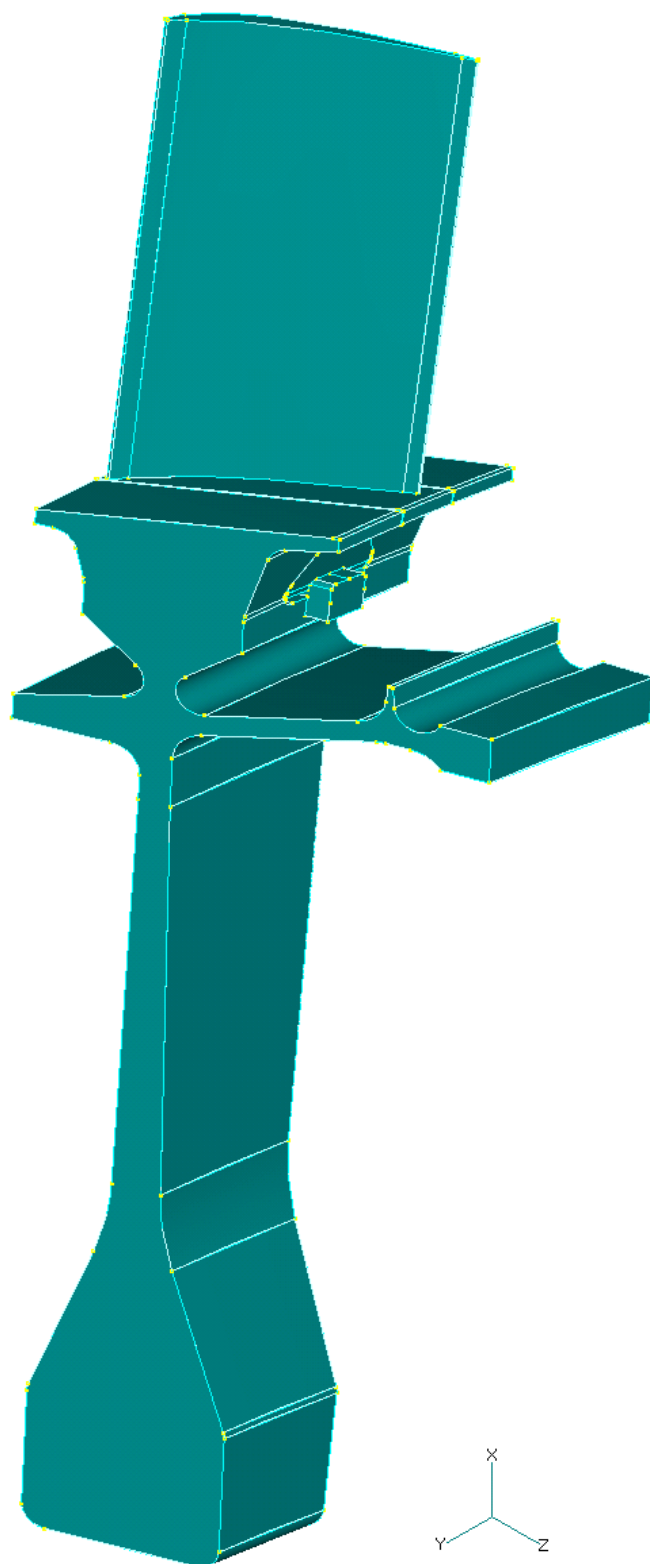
Загальний вигляд збірки сегмента диска, лопатки і стопорної пластини
